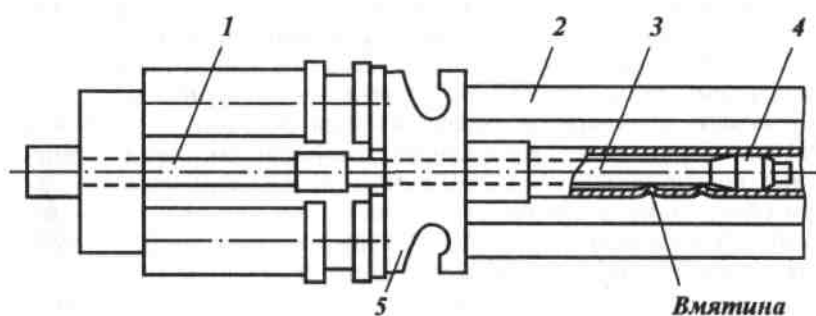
Схема правки вмятин в корпусе турбобура: 1 - удлинитель; 2 - рама пресса; 3 - вал; 4 - калибрующее кольцо; 5 – элеватор
